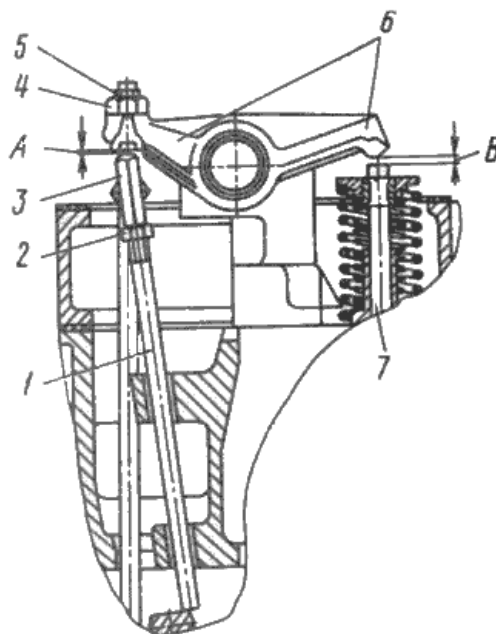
Схема регулировки зазоров клапанов и декомпрессионного механизма двигателя Д-130Т
